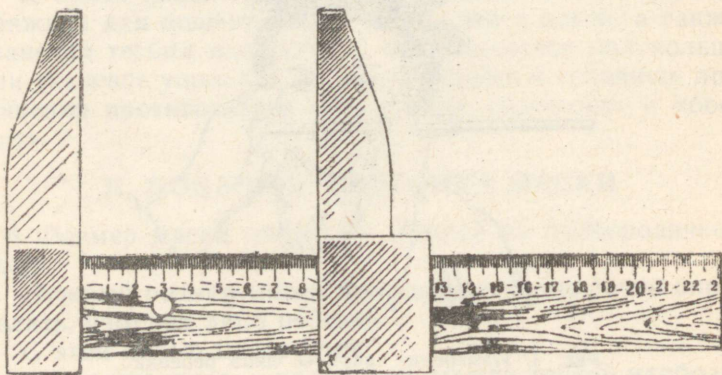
Штангенциркуль, изготовленный из ученической линейки.
